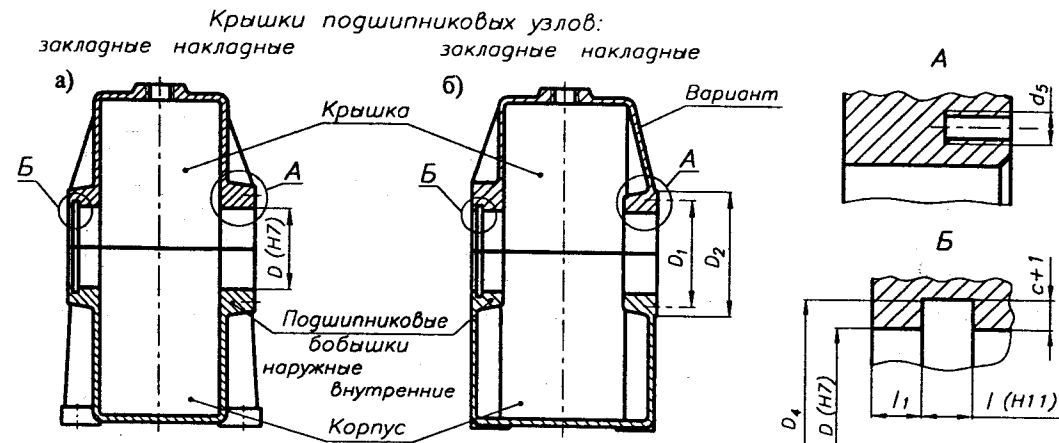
Поперечные сечения по подшипниковым узлам цилиндрического редуктора, выполненного с расположением подшипниковых бобышек:
